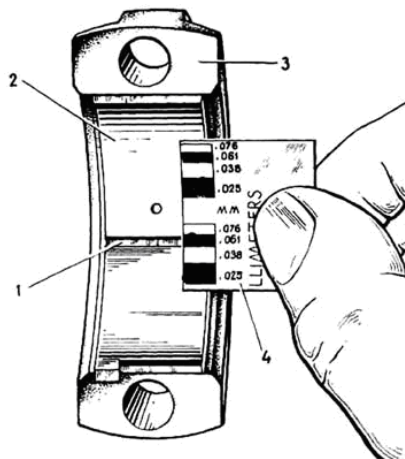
Измерение с помощью шкалы ширины калиброванной проволоки после сплющивания: 1– калиброванная проволока, 2 – вкладыш, 3 – крышка шатунного подшипника, 4 – шкала для калиброванной проволоки
